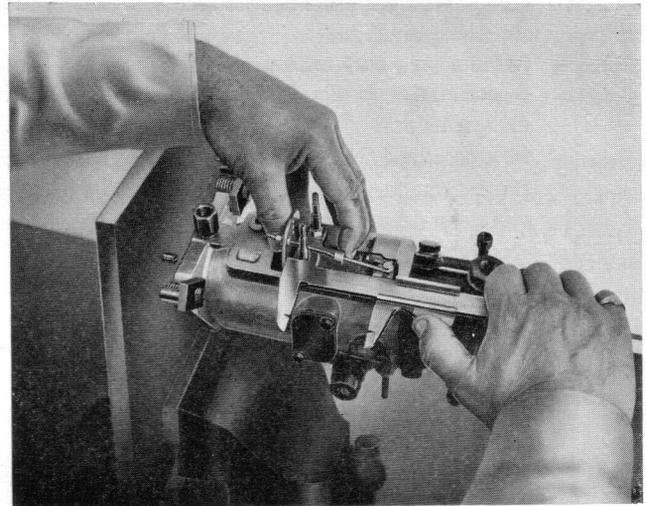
Réglage de la tringlerie des régulateurs mécaniques
